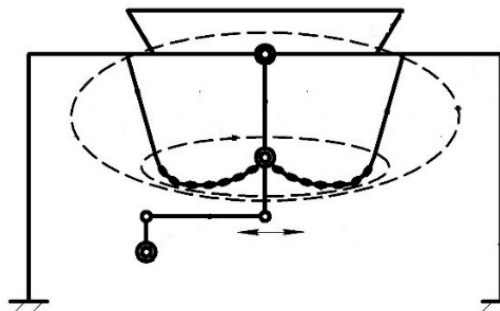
Конструктивная схема опытного образца цепного агрегата
